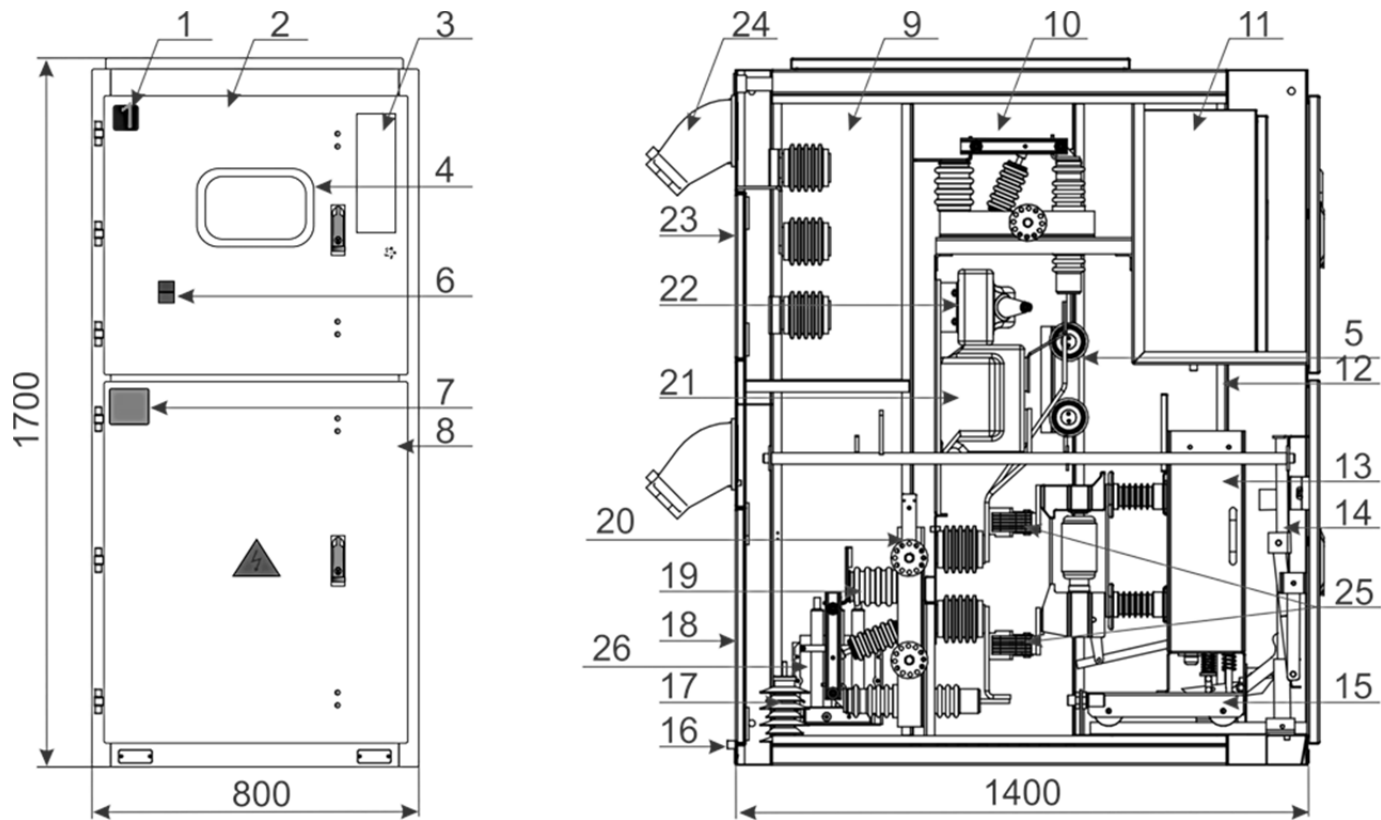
Вид и устройство шкафа КРУ-РН
